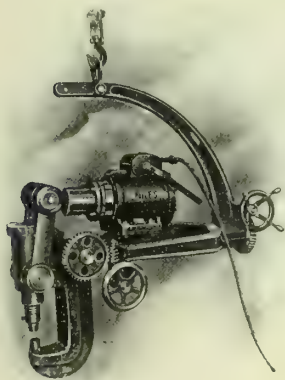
Nietmaschine für Feuerloch- und Fussringe
